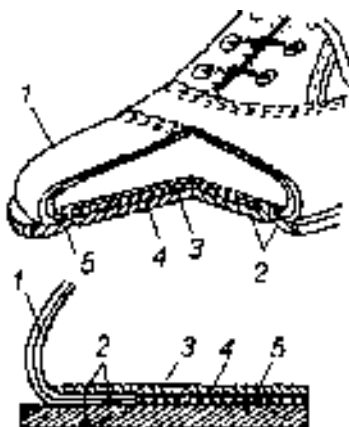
Гвоздевой метод крепления: а – разрез обуви; б – схема крепления: 1 – заготовка; 2 – гвозди; 3 – стелька; 4 – простипка; 5 – подошва
